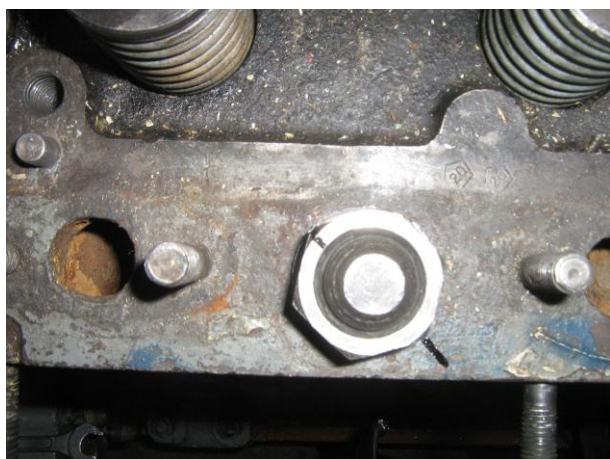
Разметка затяжки гаек крепления крышки цилиндра до отказа
